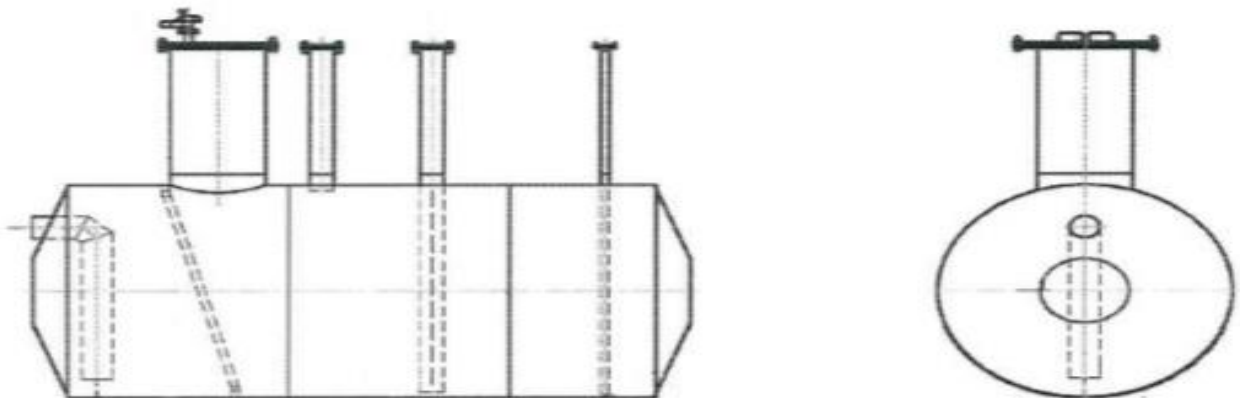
Эскиз общего вида резервуара РГС-10.
